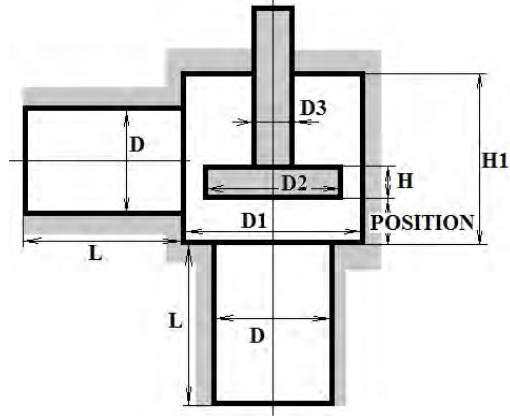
Разрез углового клапана [1; 2]. Авторский рисунок.
